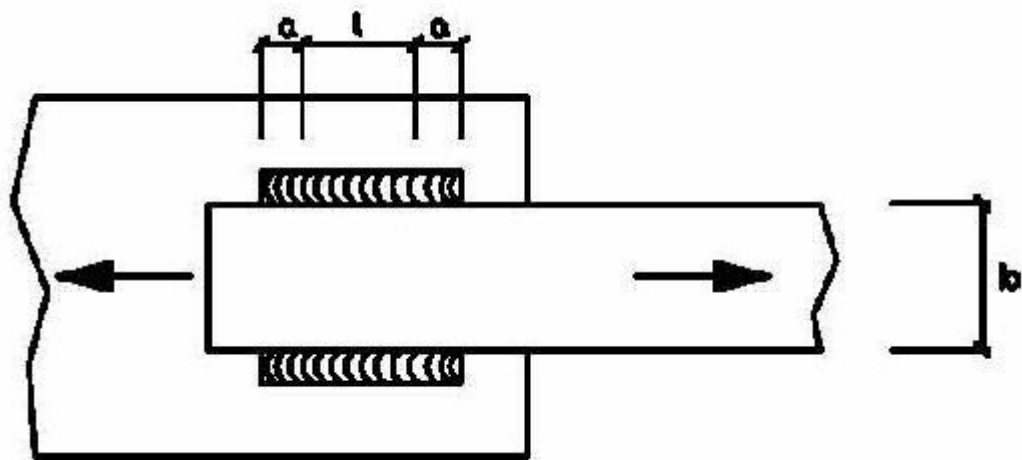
Denominación de los tipos de soldadura
